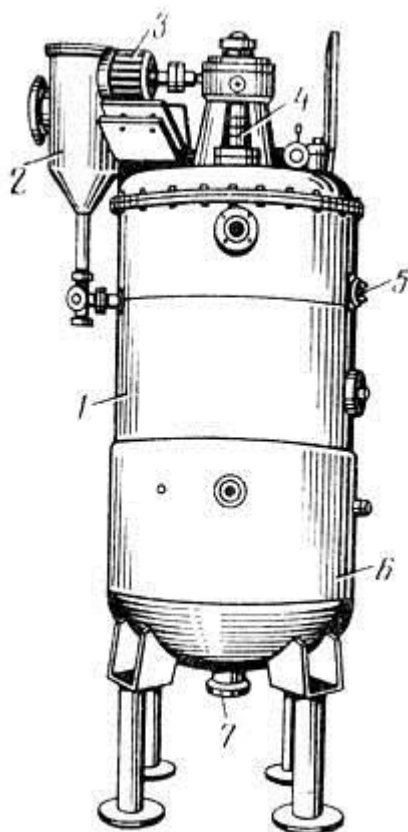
Вакуум-аппарат МЗС-320М: 1 - корпус; 2- ловушка; 3 - электродвигатель; 4 - мешалка; 5 - загрузочный штуцер; 6 - паровая камера; 7 - разгрузочный патрубок
